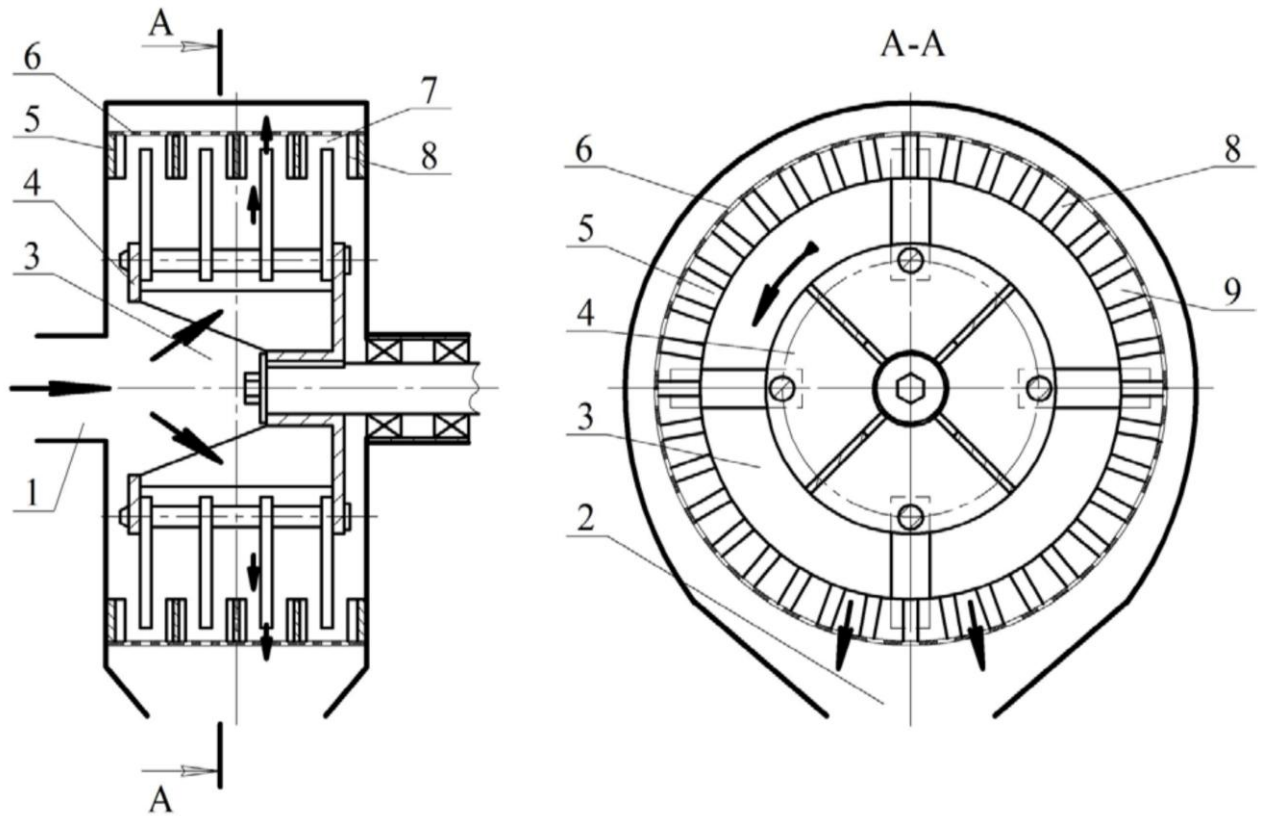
Конструктивна схема подрібнювача згідно розробки: 1 - завантажувальний патрубок; 2 - розвантажувальний патрубок; 3 – подрібнююча камера; 4 - ротор; 5 - дека; 6 - класифікатор; 7 - кільцеві канали; 8 - поперечні поверхні дек; 9 - ребра дек
